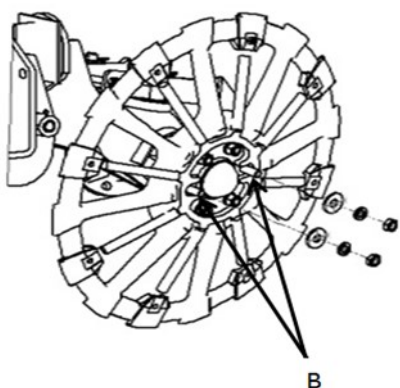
Добавление или удаление колес наполнителя в центре горы
